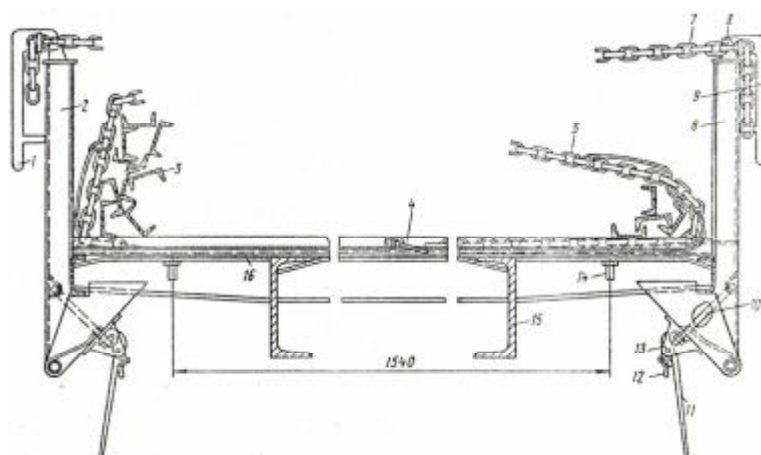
Приспособление для увязки длинномерного металла в бортовых платформах
